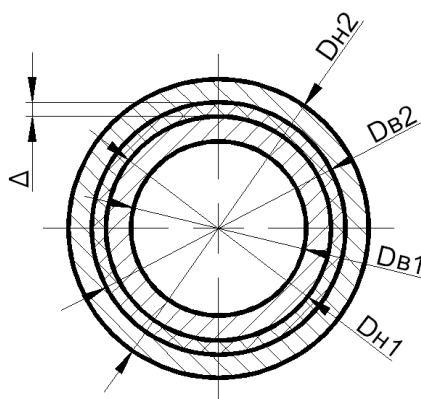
Поперечное сечение двухслойного гидроцилиндра
